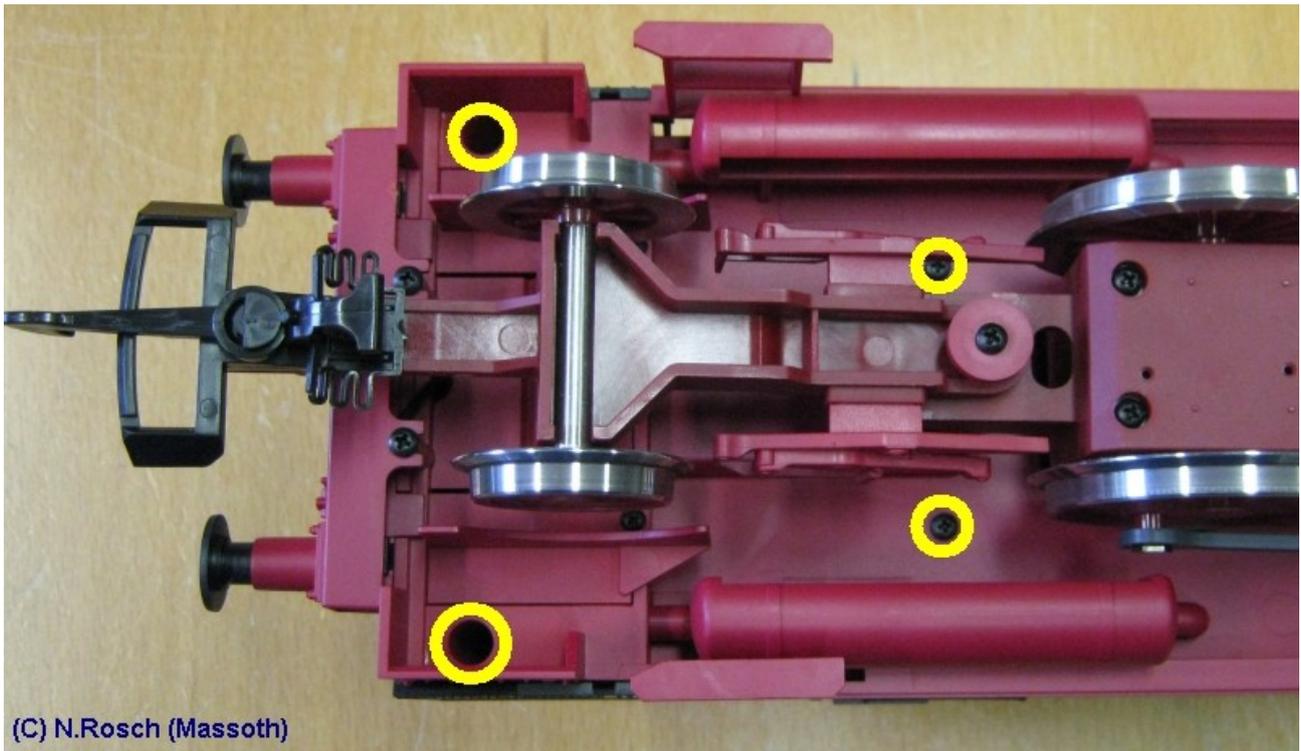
Entfernen der 4 Schrauben im Fahrzeugboden
